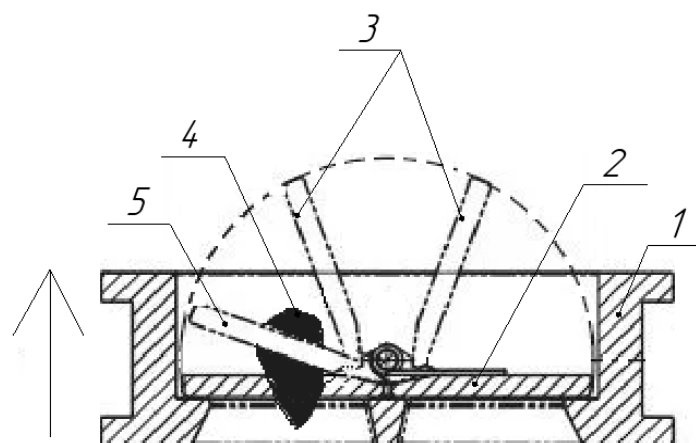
Конструкция межфланцевого обратного клапана (<https://vseotrube.ru/ventili-i-zadvizhki/klapan-obratnyj-mezhflantsevoj>): 1 – корпус клапана, 2 – створки клапана в закрытом положении, 3 – створки клапана в открытом положении, 4 – механическая примесь, 5 – створка клапана в промежуточном состоянии
